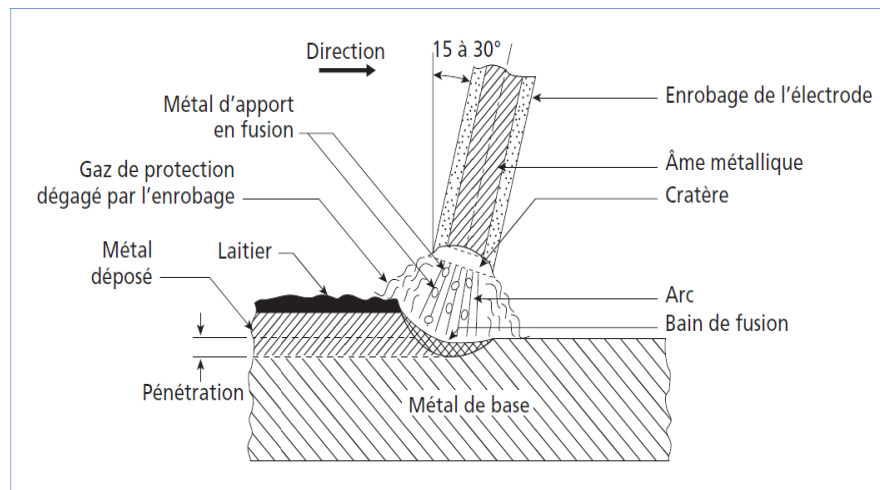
Principe de soudage à l'arc avec électrode enrobée (SMAW)[24]
